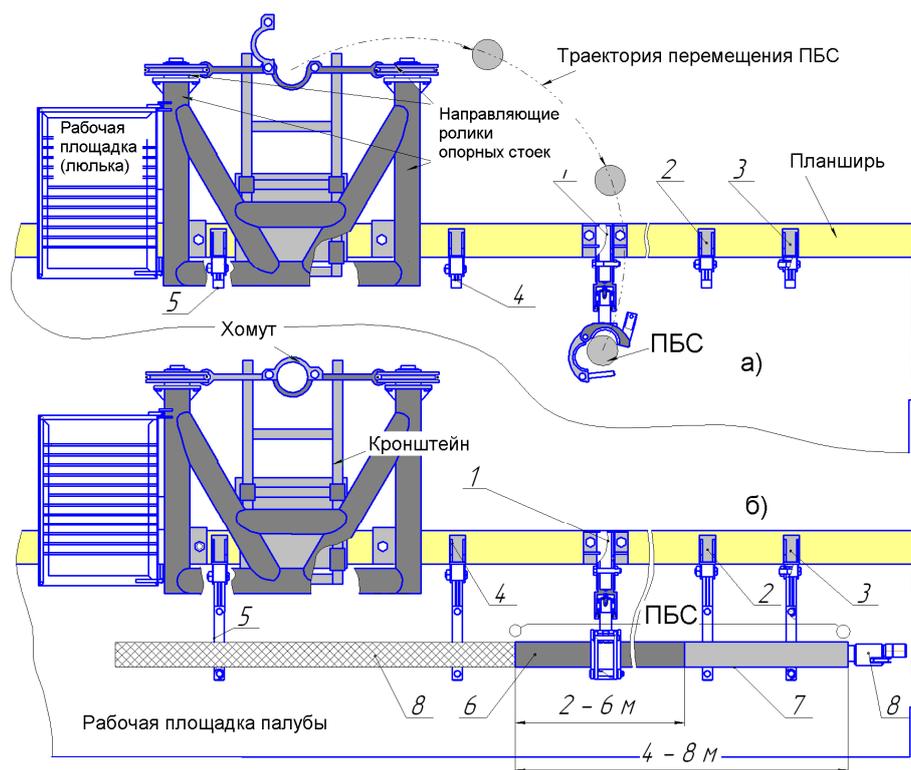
План размещения разработанного технологического оборудования установки УМБ-130М: 1 – кантователь; 2, 3, 4, 5 – опорные подставки; 6 – колонковый набор ПБС; 7 – Гидроударник ПБС; 8 – извлеченная керноприемная труба; а – схема вертикального перемещения ПБС после освобождения из хомута; б – горизонтальное положение ПБС на опорных подставках
